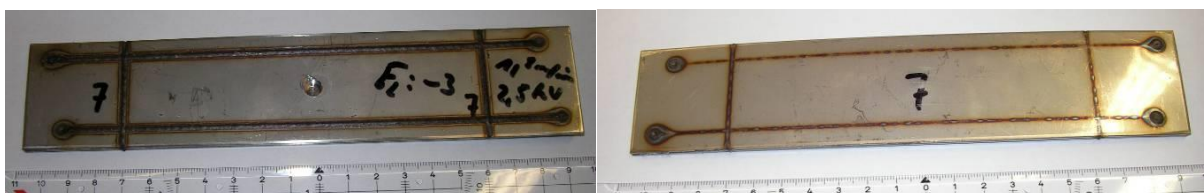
Vorder- und Rückansicht einer Schweißprobe für He-Lecktest Untersuchung
